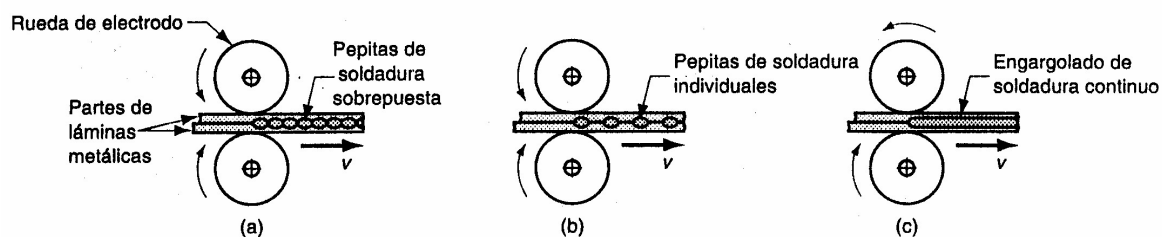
Tipos de soldadura engargolada con electrodo tipo rueda: (a) soldadura engargolada por resistencia convencional, puntos sobrepuestos, (b) soldadura de punto con rodillo, (c) soldadura engargolada constante.
